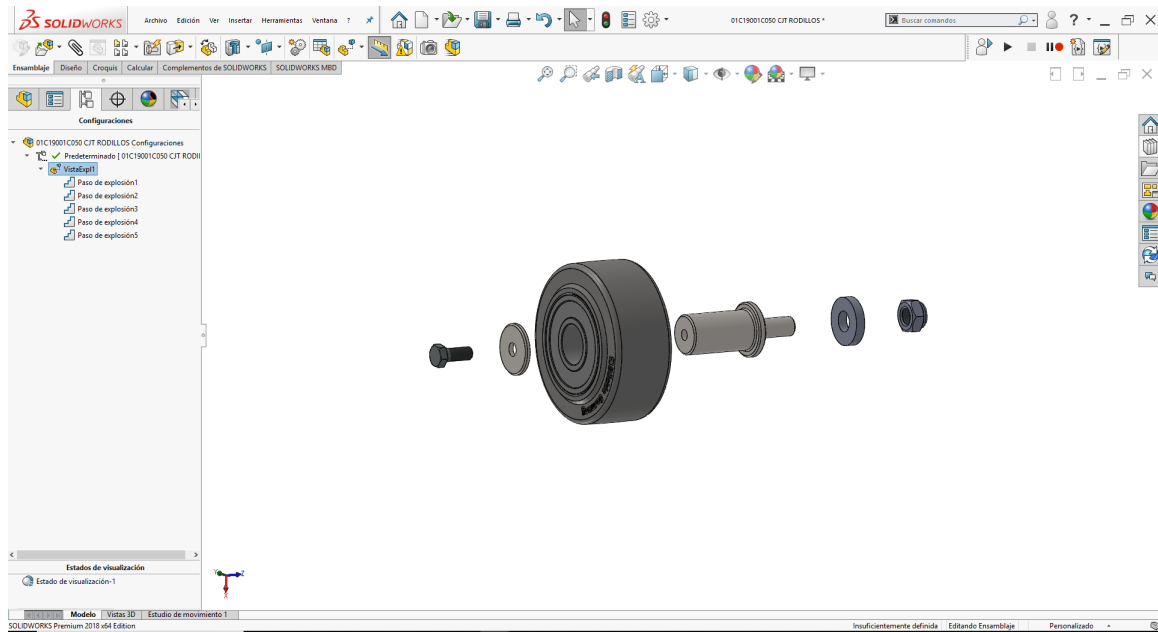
Esquema general y posiciones rodillos, vista explosionada
